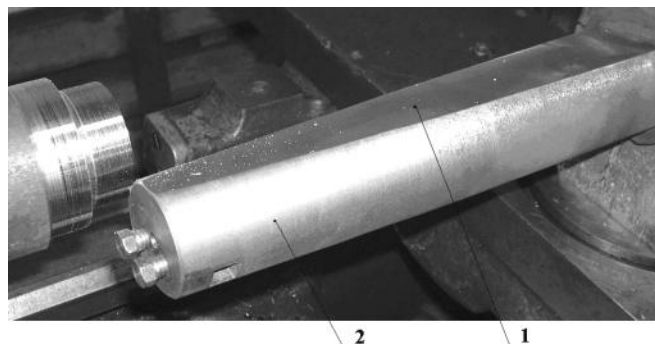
Борштанга з орієнтованою жорсткістю для підвищення сталості токарної обробки під час випробувань на стенді, виконаному на базі токарного верстата
